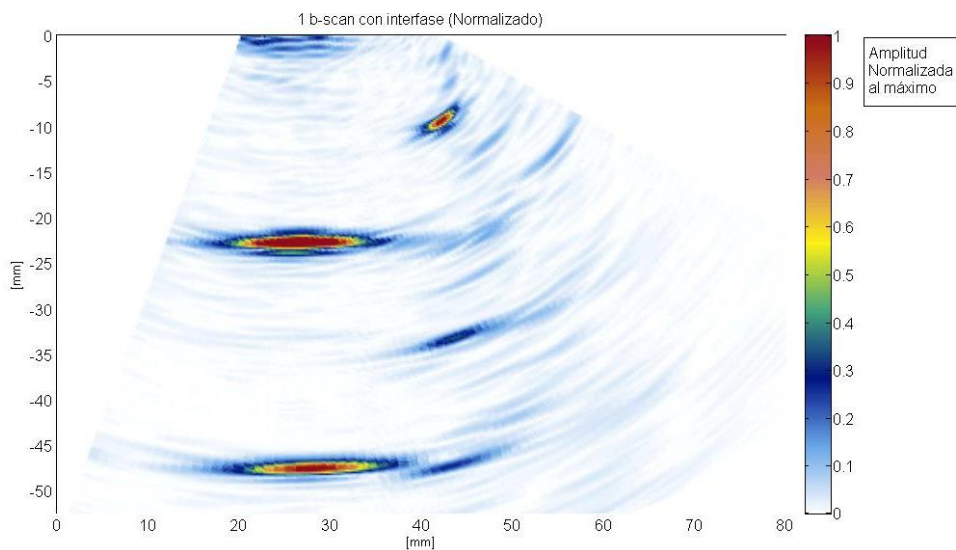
Imagen S-Scan del cordón de soldadura de acero inoxidable austenítico.
